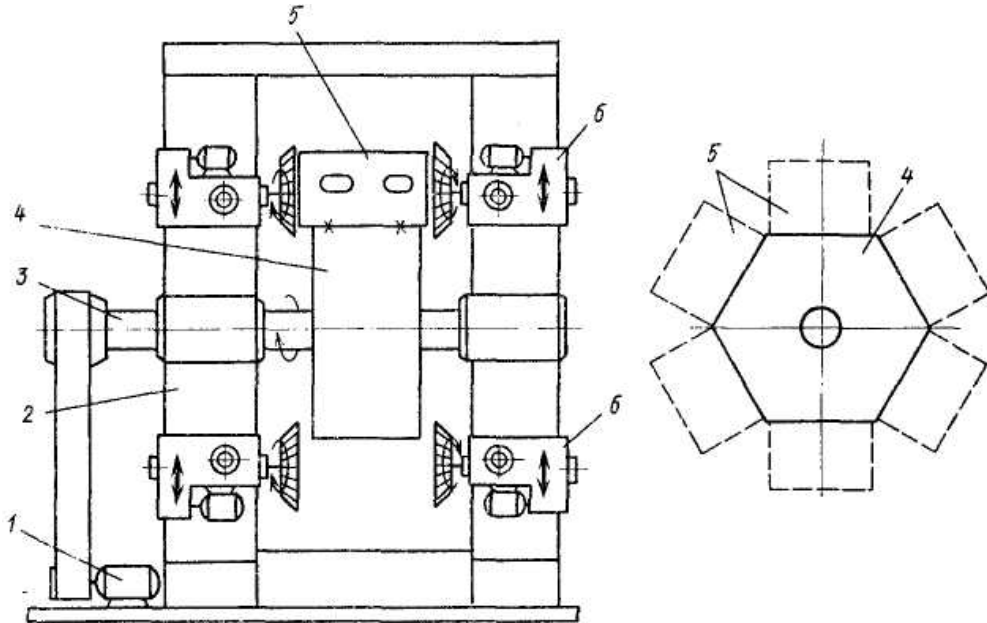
Принципиальная схема барабанно-фрезерного станка:
